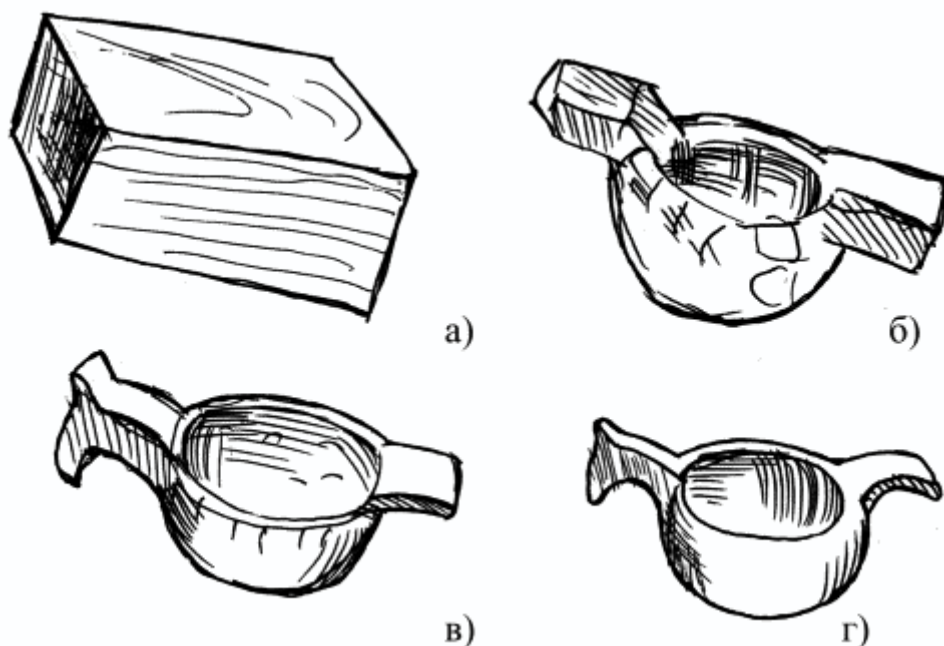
Последовательность резьбы ковша: а – разметка чурака; б – обрубка; в – наружная черновая обрубка; г – чистовая обработка
